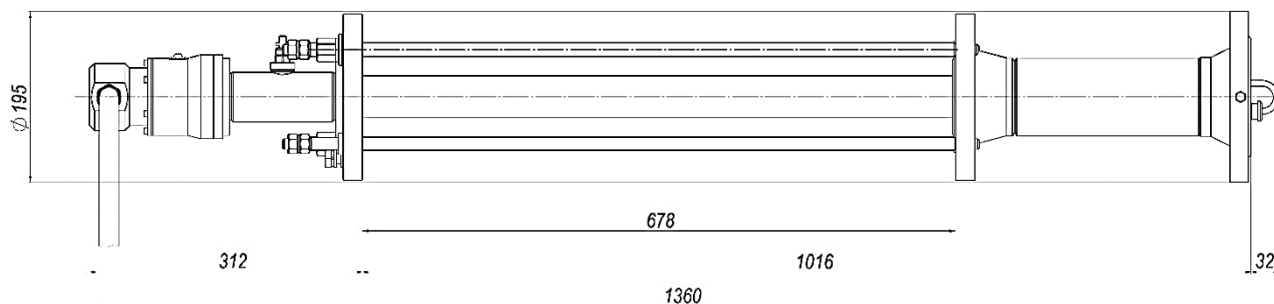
Габаритные размеры приемопередатчика КТМ100 ПР ЛБ (с установочным приспособлением)
